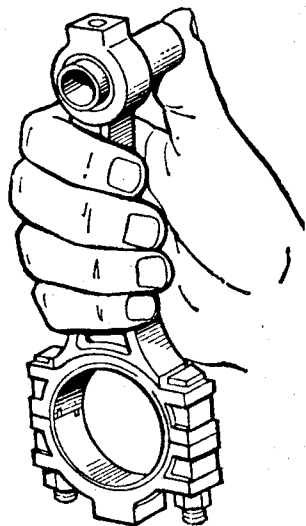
Проверка подбора поршневого пальца к втулке верхней головки шатуна
